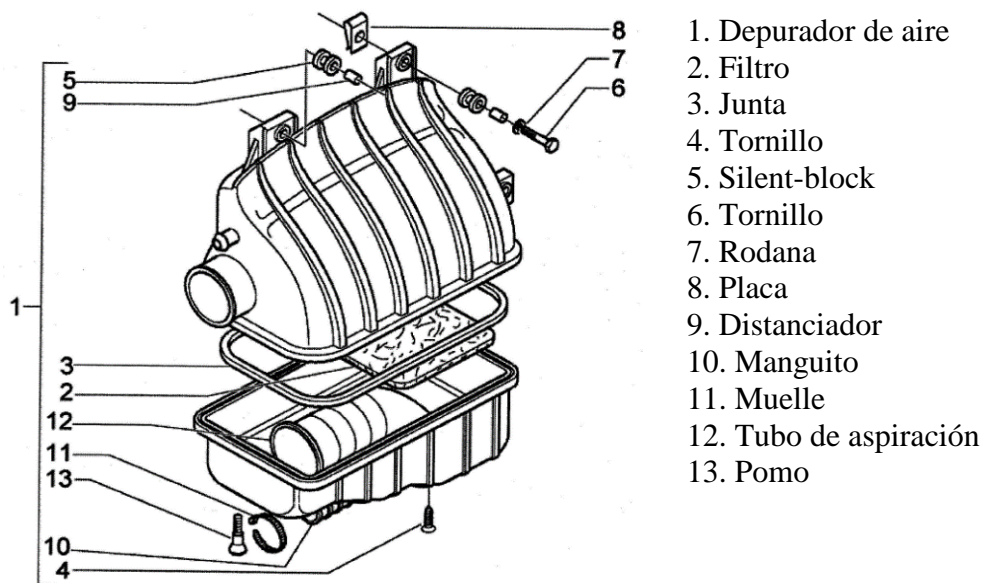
Filtro de aire de motor Piaggio 500cc
